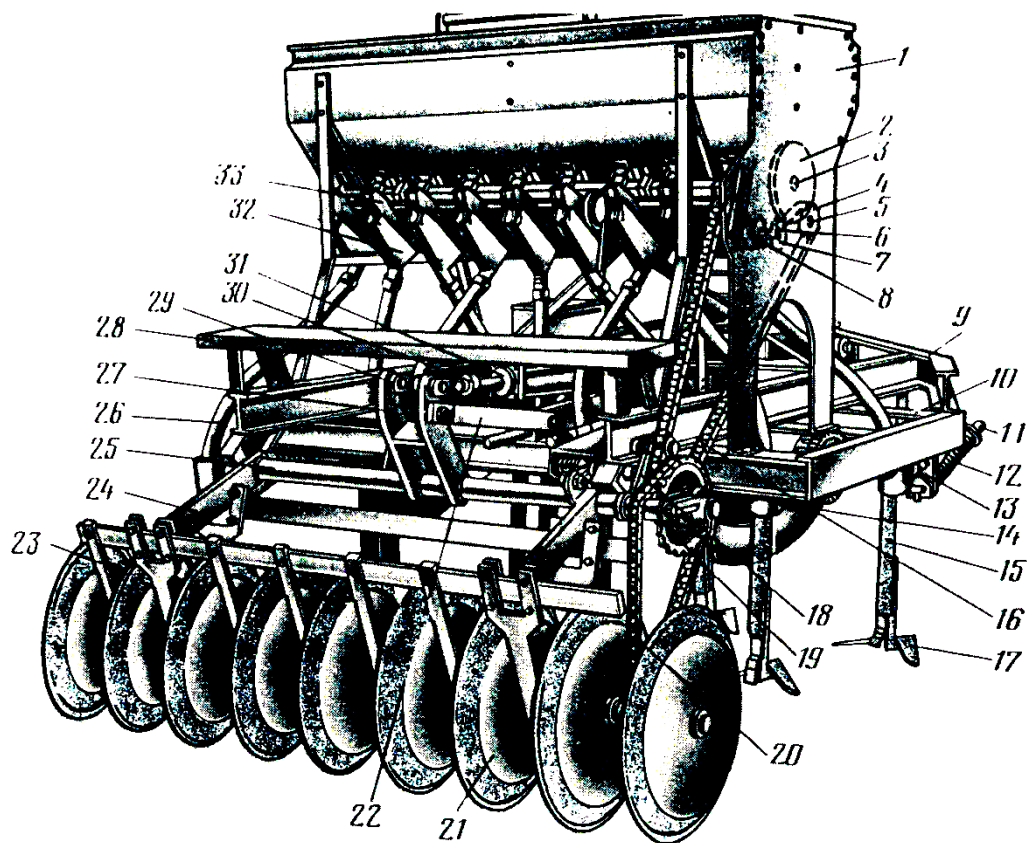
Сеялка-культиватор СЗС-2,1:1 — зернотуковый ящик; 2 — зубчатое колесо вала туковых аппаратов; 3 — вал туковых аппаратов; 4 — звездочка вала туковых аппаратов; 5 — вал зерновых аппаратов; 6 — промежуточный валик; 7 — зубчатое колесо промежуточного валика; 8 — звездочка промежуточного валика; 9 — рама; 10 — поперечный брус; 11 — стяжной болт; 12 — пружина; 13 — кронштейн сошника; 14 — опорное колесо; 15 — сошник; 16 — верхняя цепь-17 — стрельчатая лапа сошника; 18 — вилка разобшителя; 19 — храповая звездочка; 20 — нижняя цепь; 21 — прикатывающие катки; 22 — транспортная планка; 23 — чистик; 24 — рама катков; 25 — вал рамы катков; 26 — семяпровод; 27 — рычаг; 28 — подножная доска; 29 — тяга; 30 — упор; 31 — гидроцилиндр 32 — воронка; 33 — туковысевающие аппараты.
